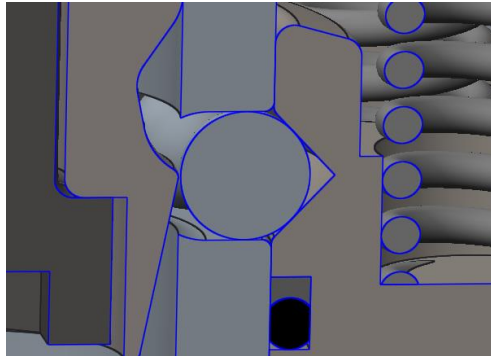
Detalle sobre la liberación de las bolas de bloqueo.
